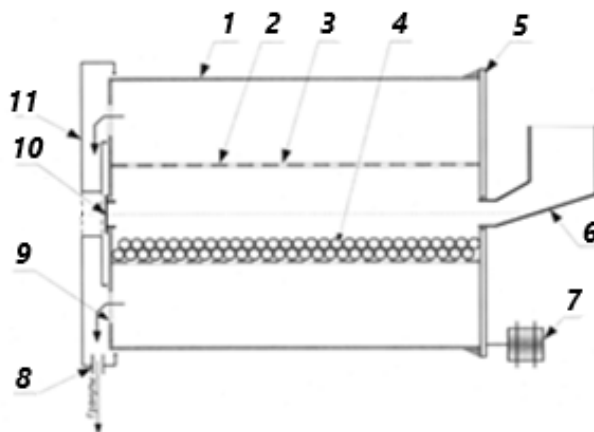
Схема барабанного экструдера с окатывателем: 1 – барабан-окатыватель гранул; 2 – барабан-экструдер; 3 – проходные отверстия; 4 – движущаяся продавливающая среда; 5 – крышка барабана; 6 – патрубок загрузки; 7 – привод вращения барабана-окатывателя; 8 – патрубок выгрузки; 9 – окно выгрузки; 10 – технологический люк; 11 – короб приема и сбора.
